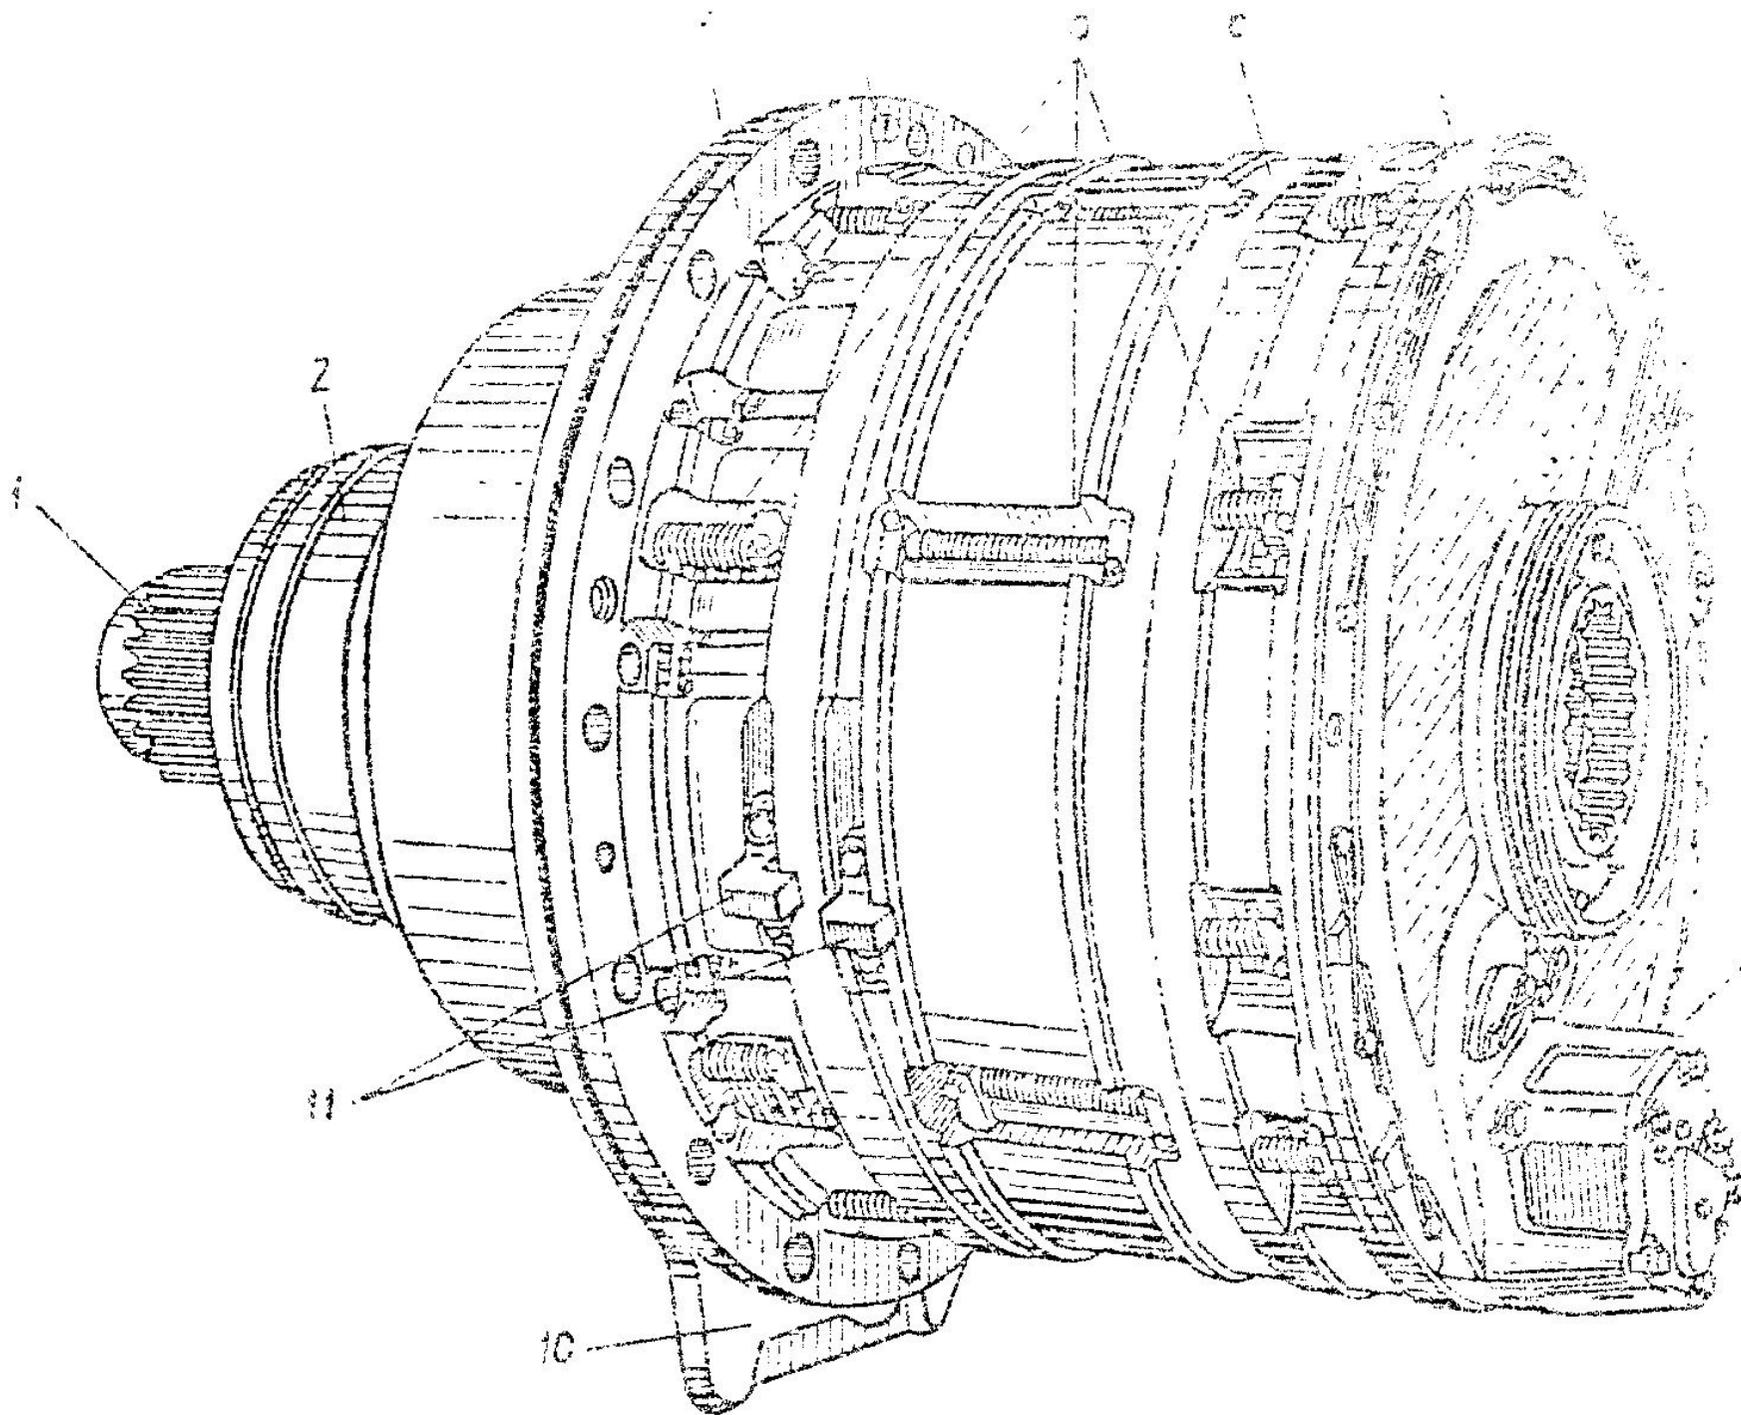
Коробка передач в сборе с бортовой передачей (9, 11) для 47-го танка.
